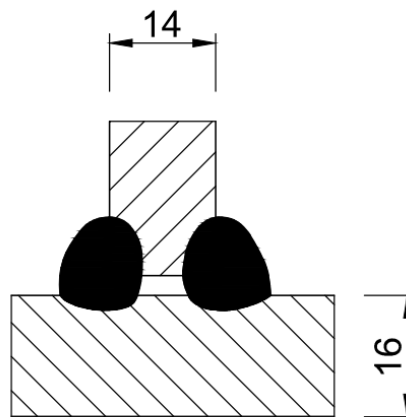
Конструктивний розріз зварного з'єднання ТЗ – УП.
